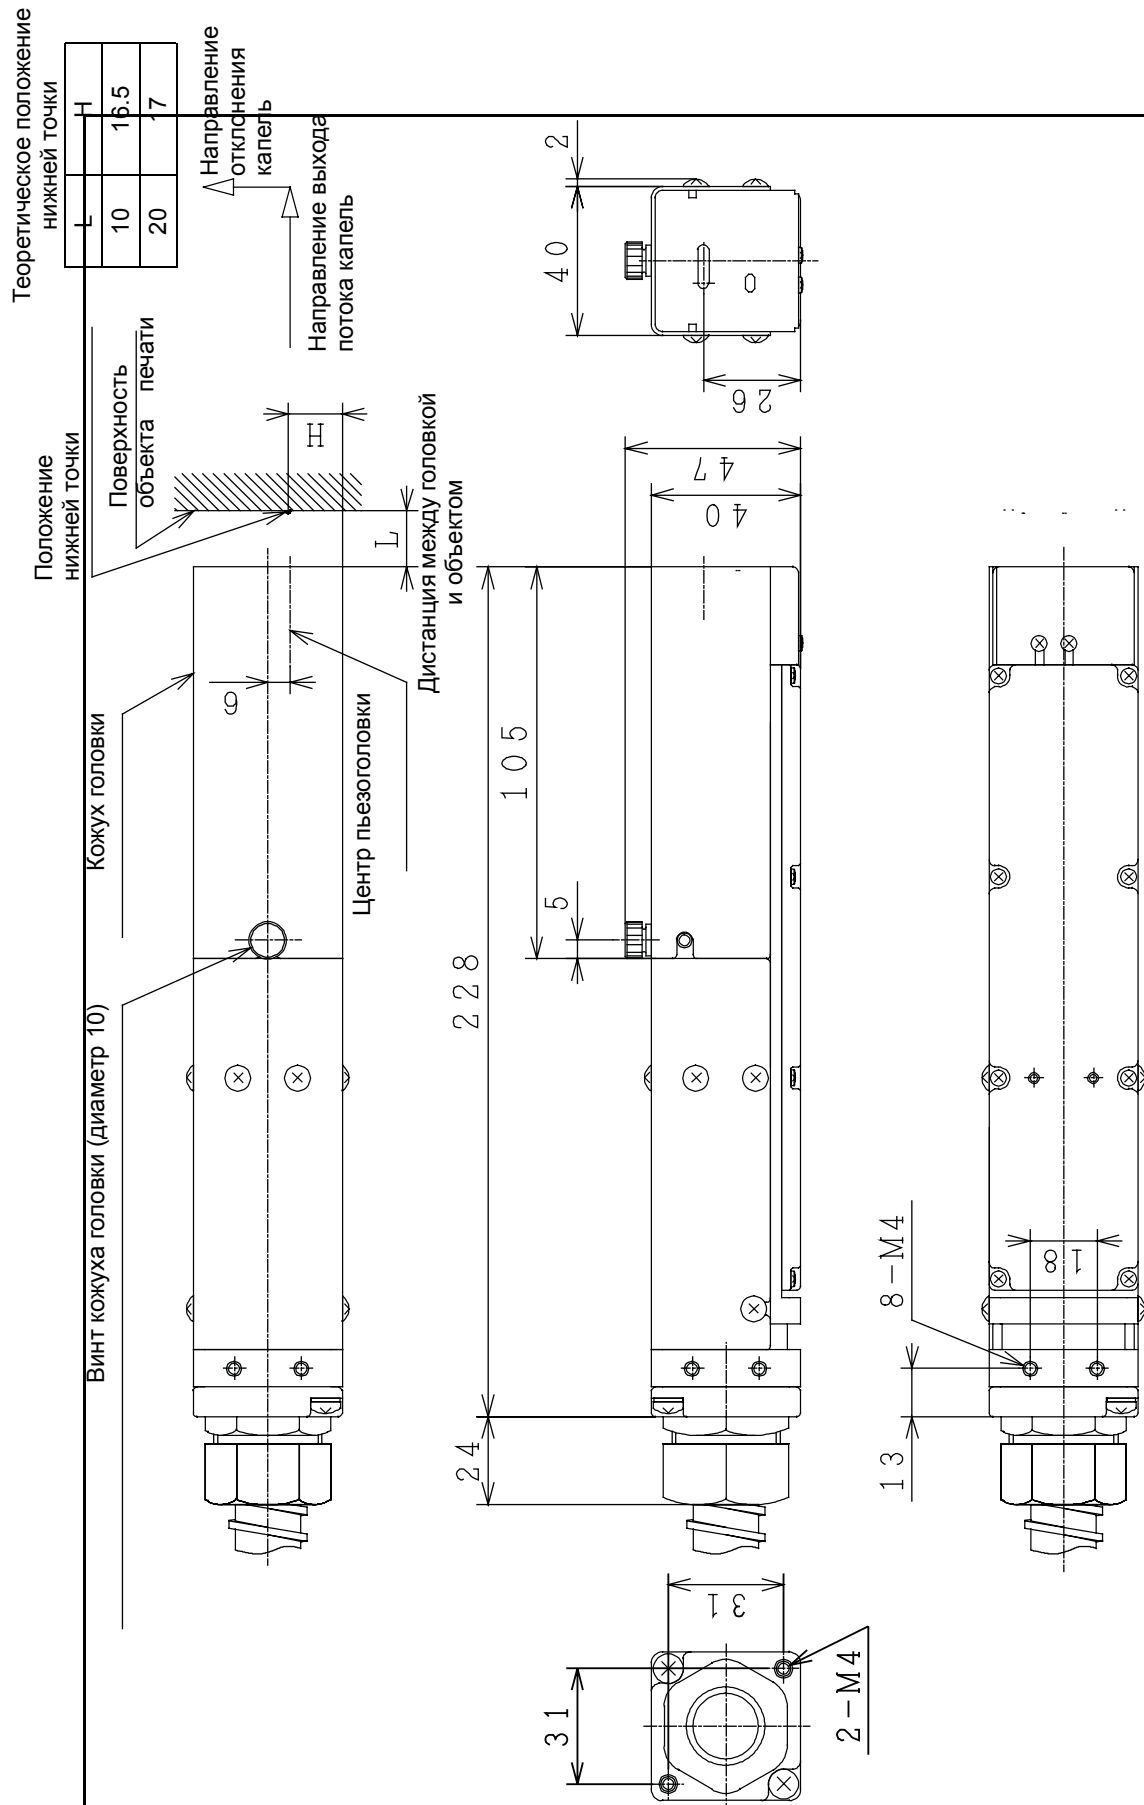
Размеры печатающей головки (согласно 65 μm)
